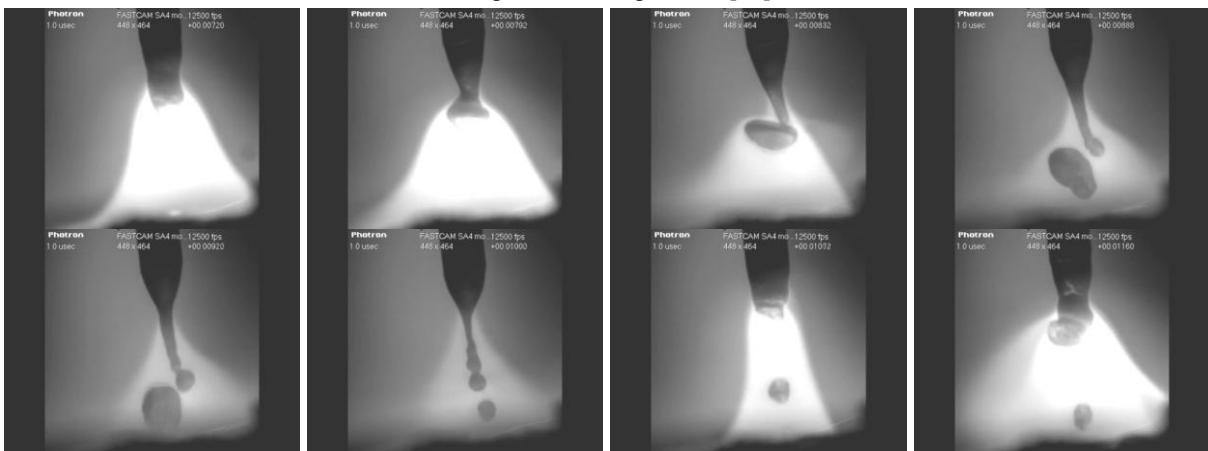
Процесс переноса металла при импульсно-дуговой сварке в среде защитных газов с произвольными параметрами на обратной полярности [13]
